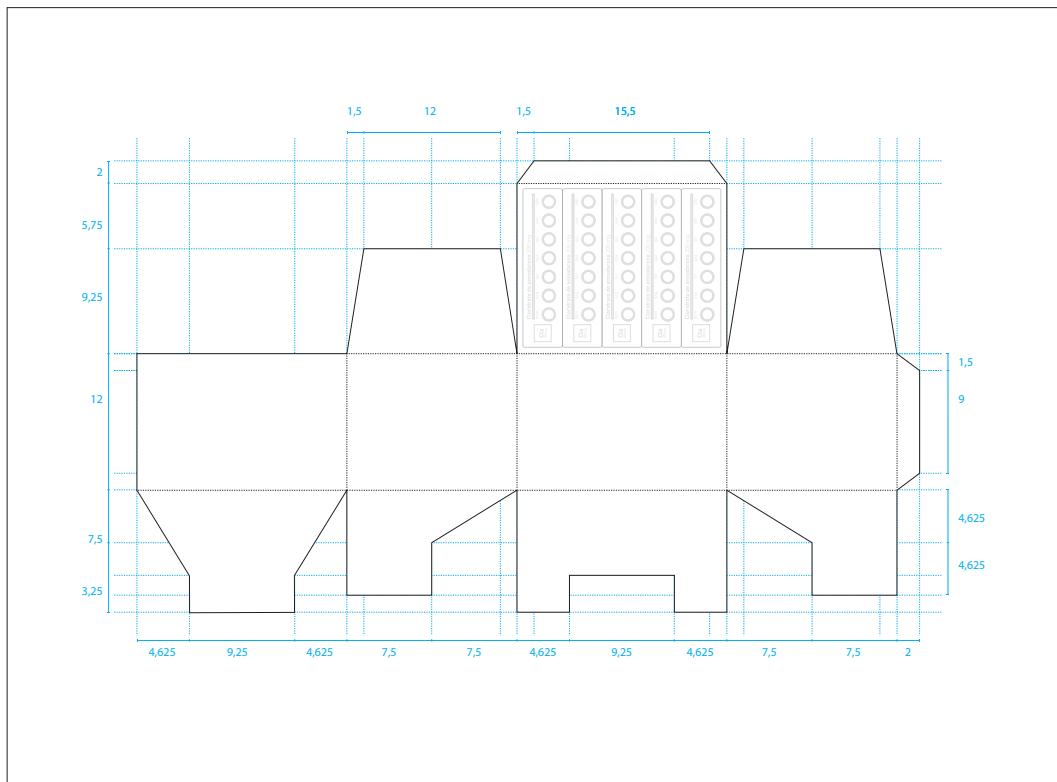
Planimetria da caixa de fornecimento do segundo blister maior (Padrão 3).
